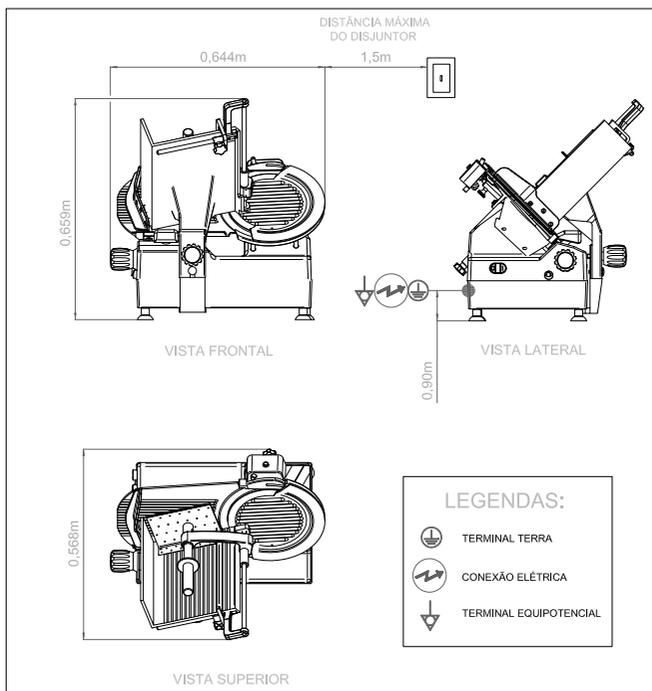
Dimensões Gerais e Instalação - Fatiador de frios automático HMD30
